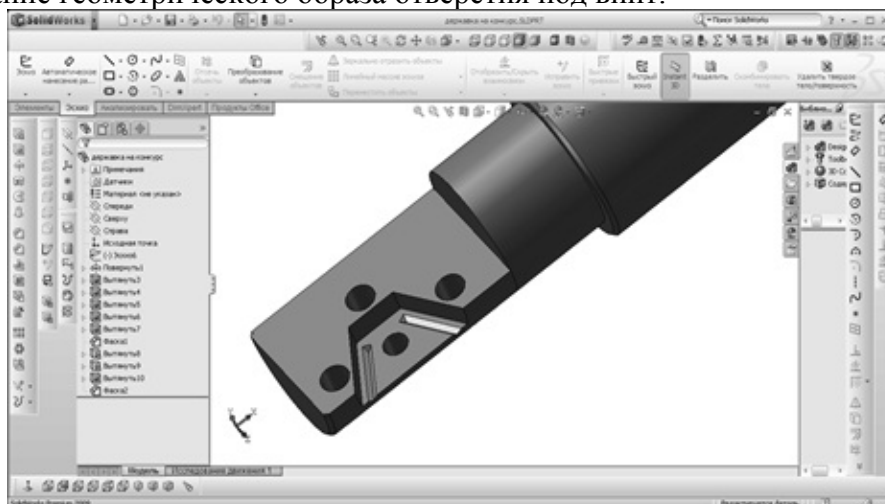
Геометрический образ корпуса сборной резьбовой головки
